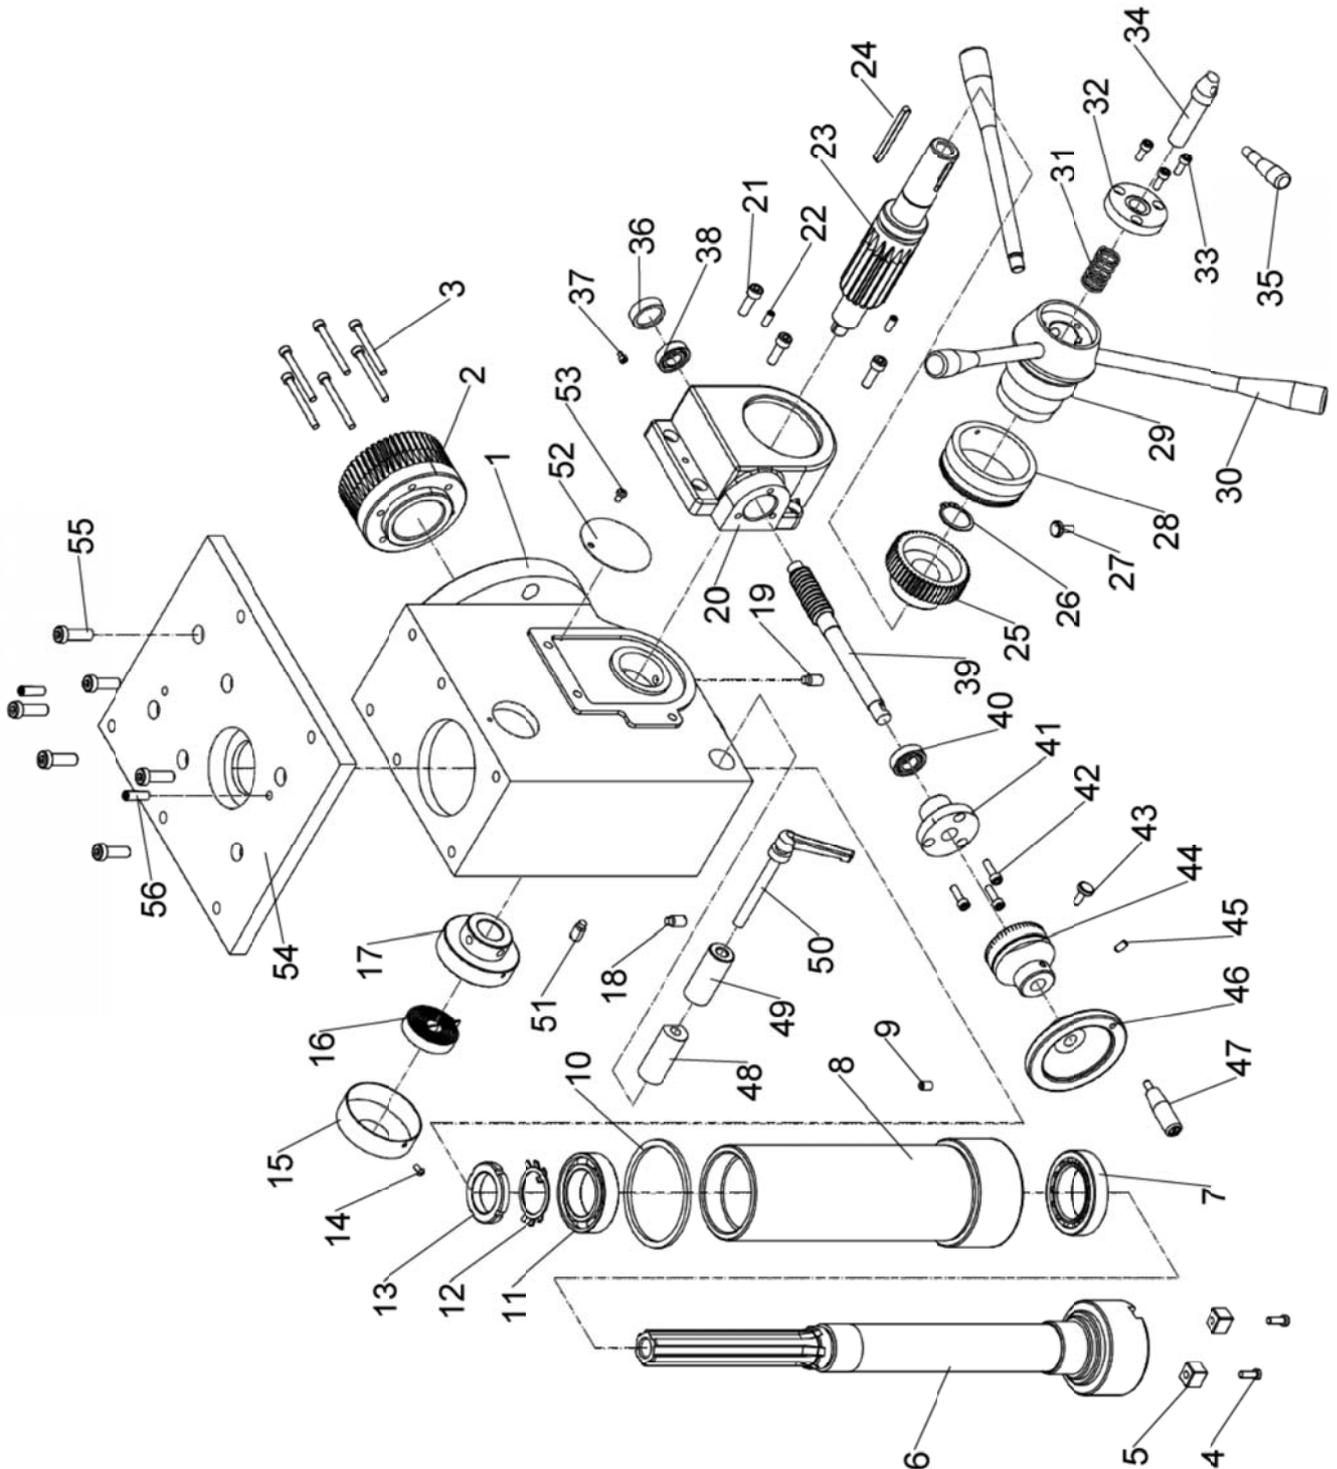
Universal Schwenkopf - Universal swiveling head
